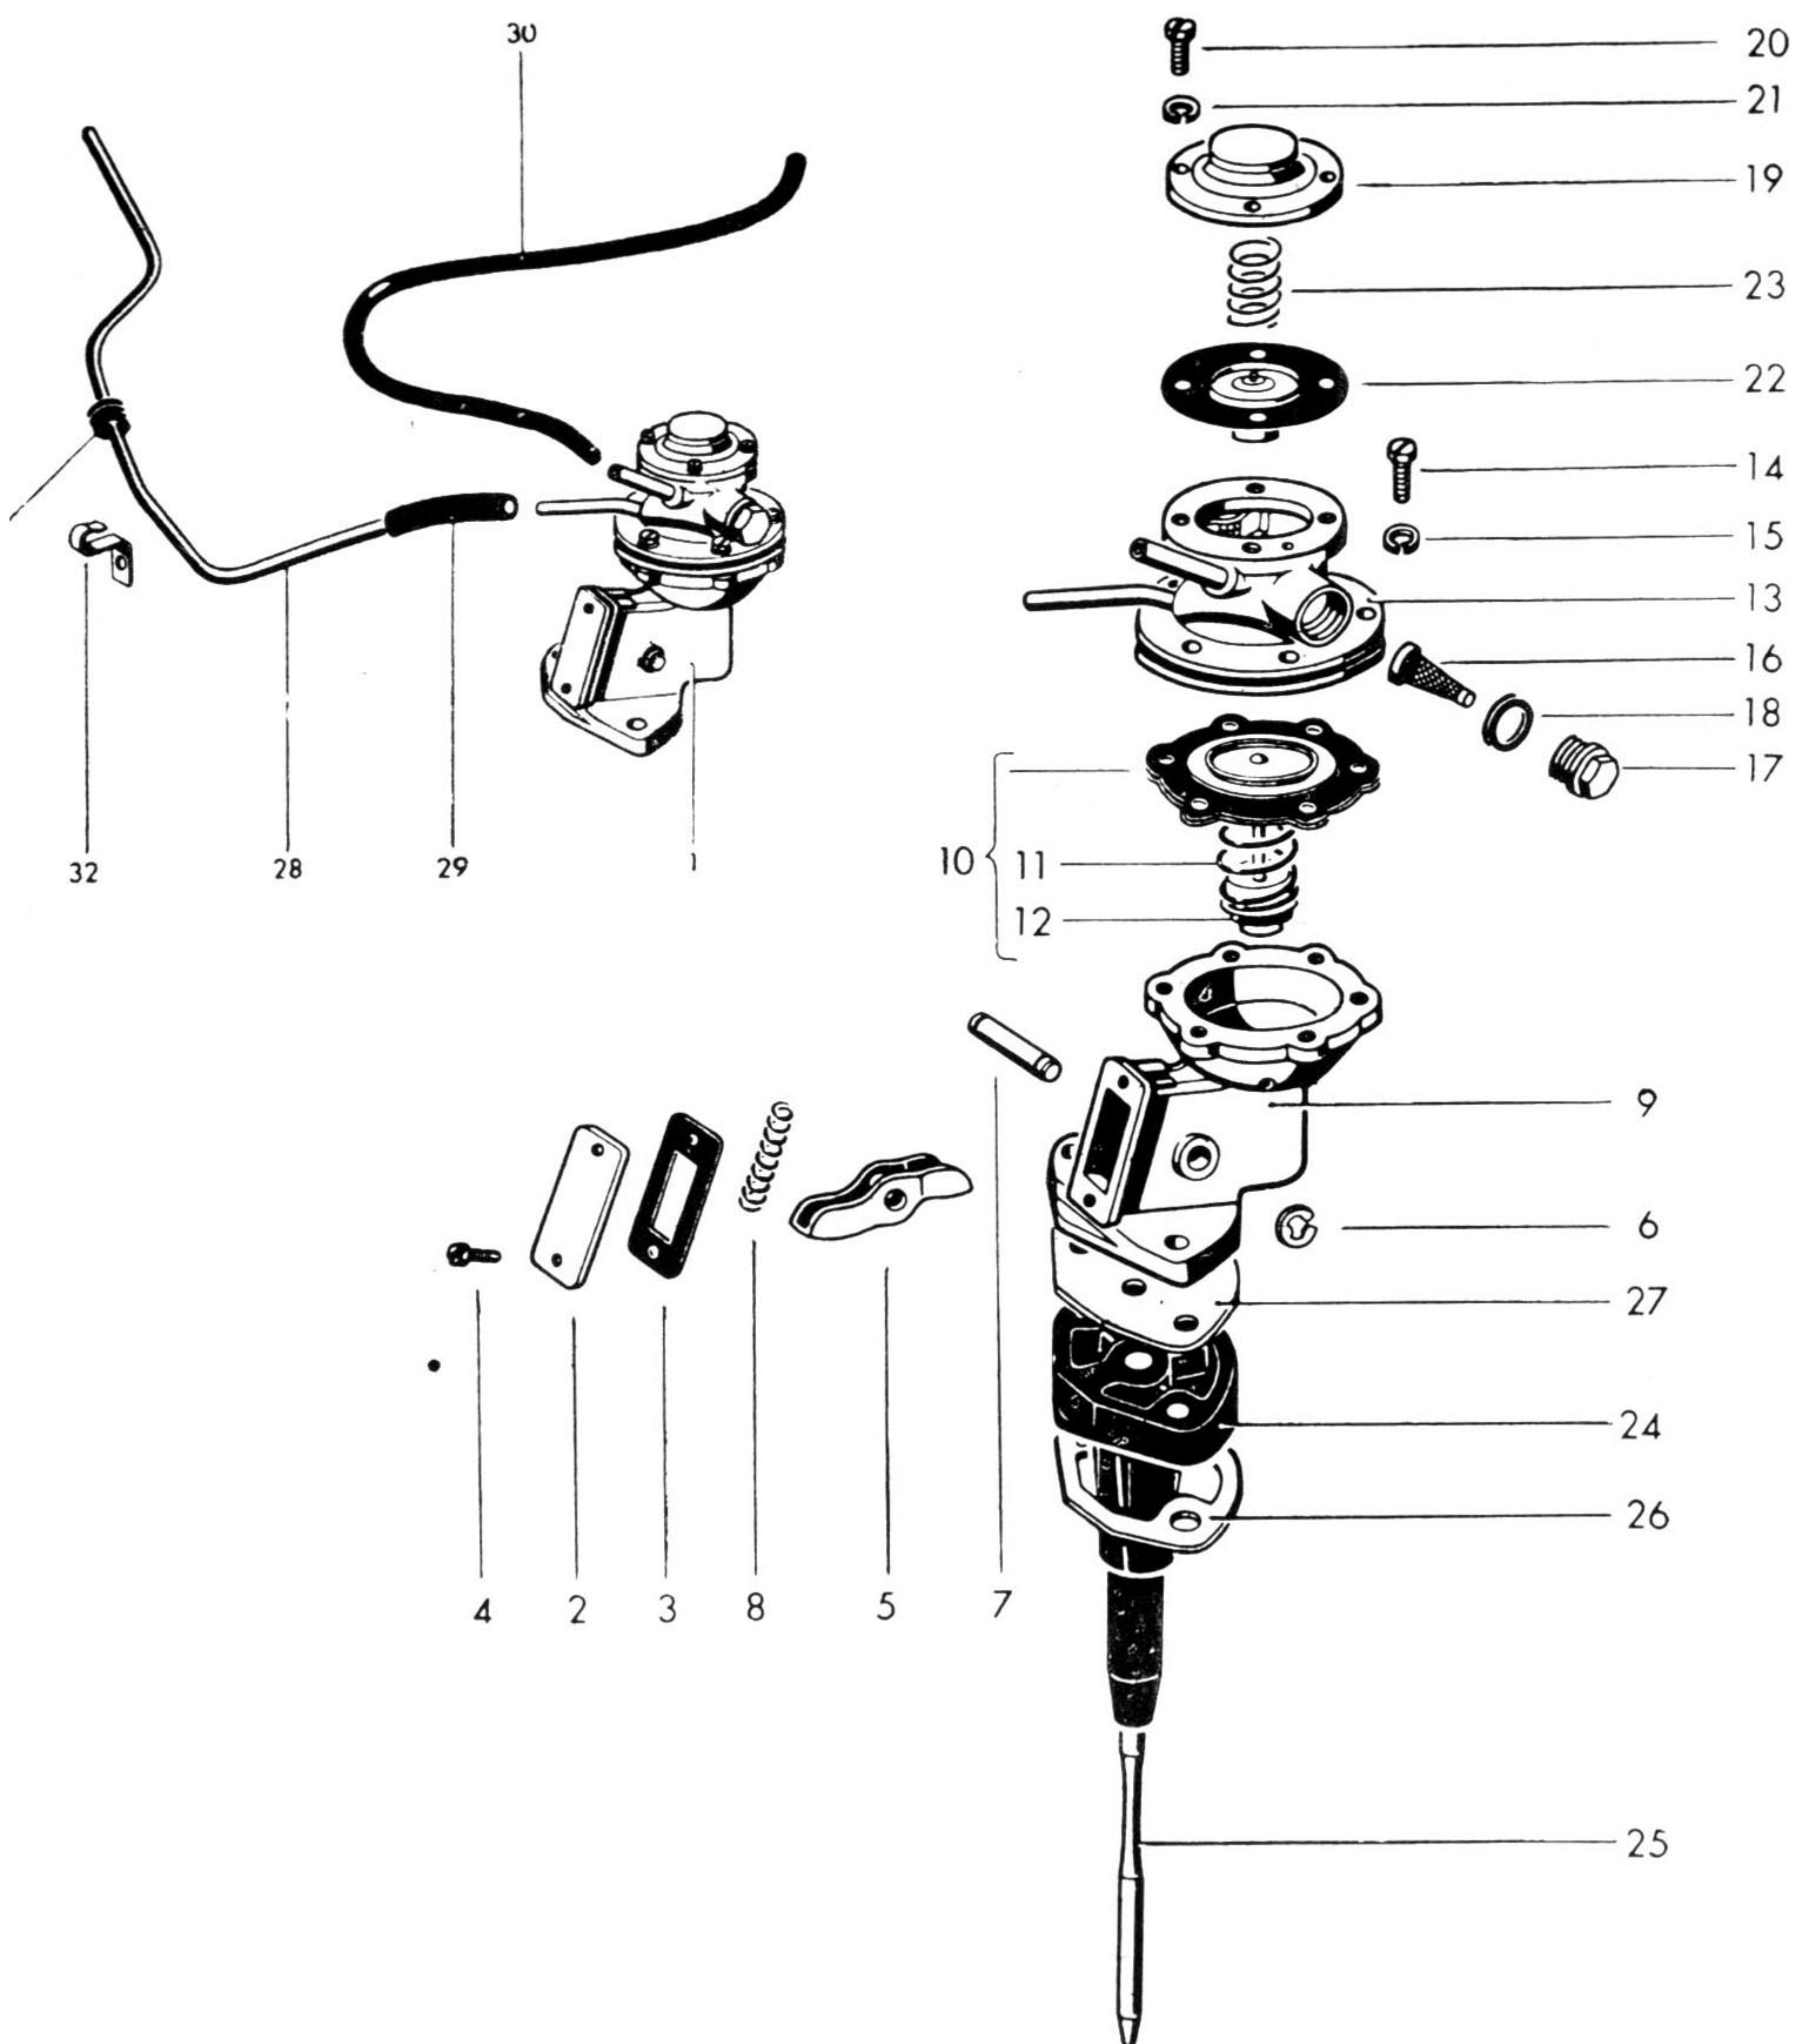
E — Bomba de gasolina do sedan “1 300” montada (acima a esquerda) e desmontada. Peças principais: 5 — balancim; 7 — eixo do balancim; 8 — mola do balancim; 9 — corpo inferior da bomba; 10 — conjunto do diafragma; 13 — corpo superior da bomba; 16 — filtro de tela; 17 — bujão do filtro; 19 — tampa; 22 — válvula de diafragma; 24 — flange de plástico; 25 — pino ou haste de comando; 27 e 28 — juntas; 29 e 30 — tubos de plástico.
